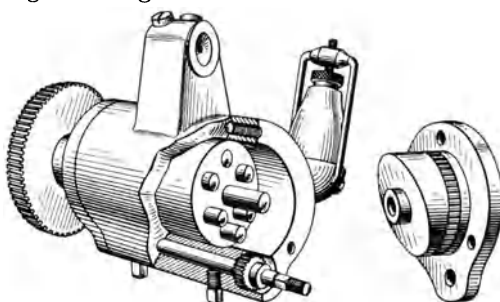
6-Zylinderpumpe von Dr. Birosi.
